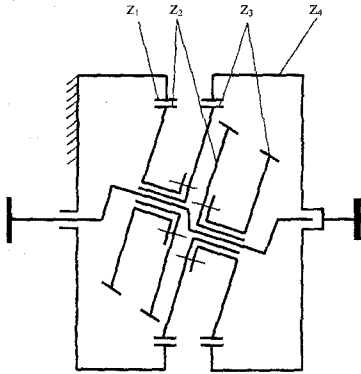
Кинематическая схема планетарного редуктора с наклонными сателлитами
